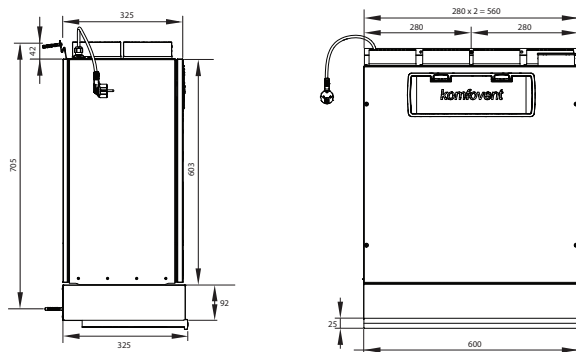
Dimensions avec la hotte de cuisine 392-12
